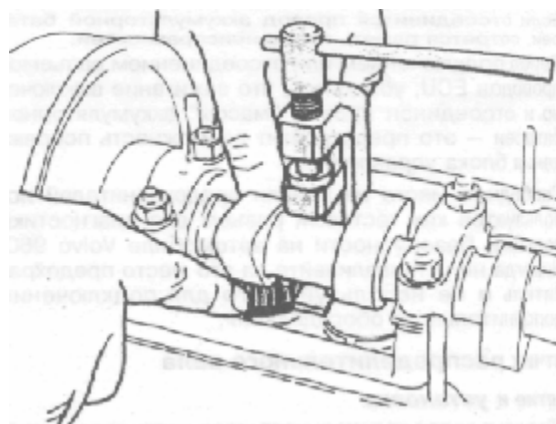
Размещение нового диска — двигатели B230F и B230FT
